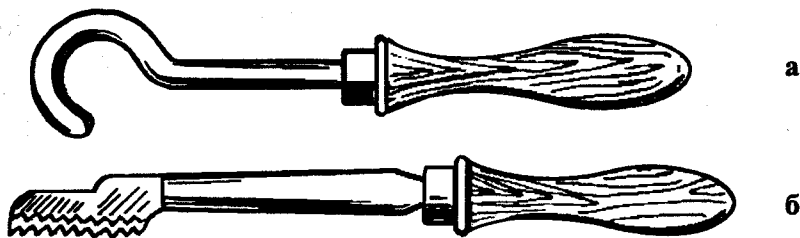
Инструменты для художественного точения: а — крючок; б — гребенка
